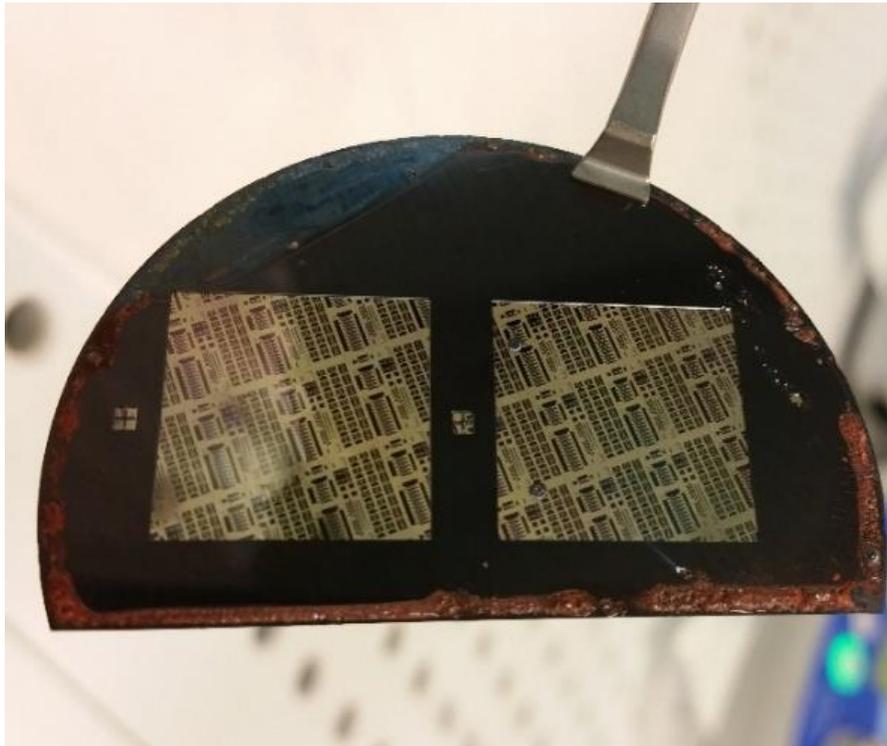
Procédé de fabrication en face arrière optimisée sur une grande surface (1,8×1,8 cm).
